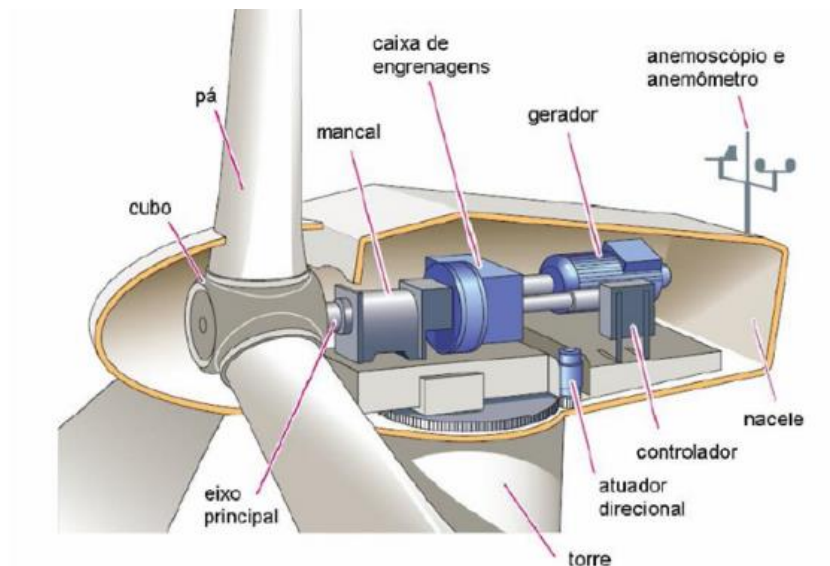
Desenho esquemático de um gerador, destacando os principais componentes.
